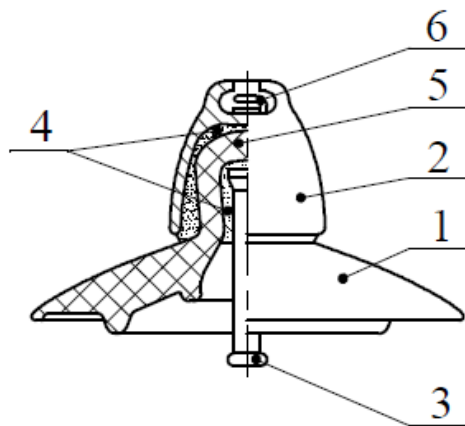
Підвісний шарнірний ізолятор з конусною голівкою: 1 – тарілка ізолятора; 2 – чавунна шапка; 3 – сталевий стрижень; 4 – цементна замазка; 5 – голівка ізолятора; 6 – замок
